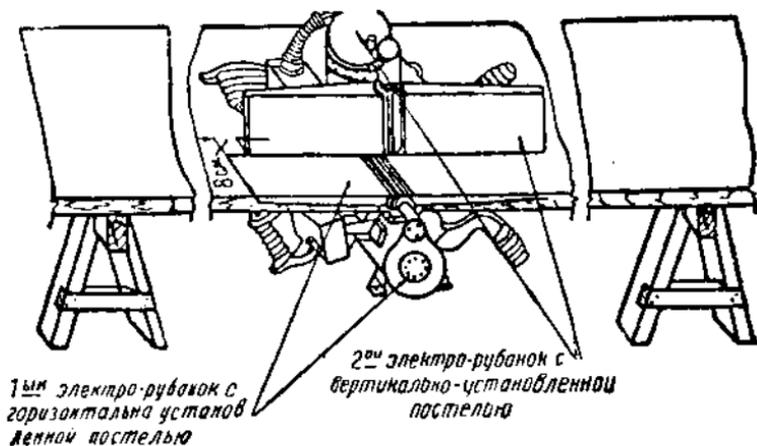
Установка двух электрорубанков на верстаке для острожки „в угол“.
